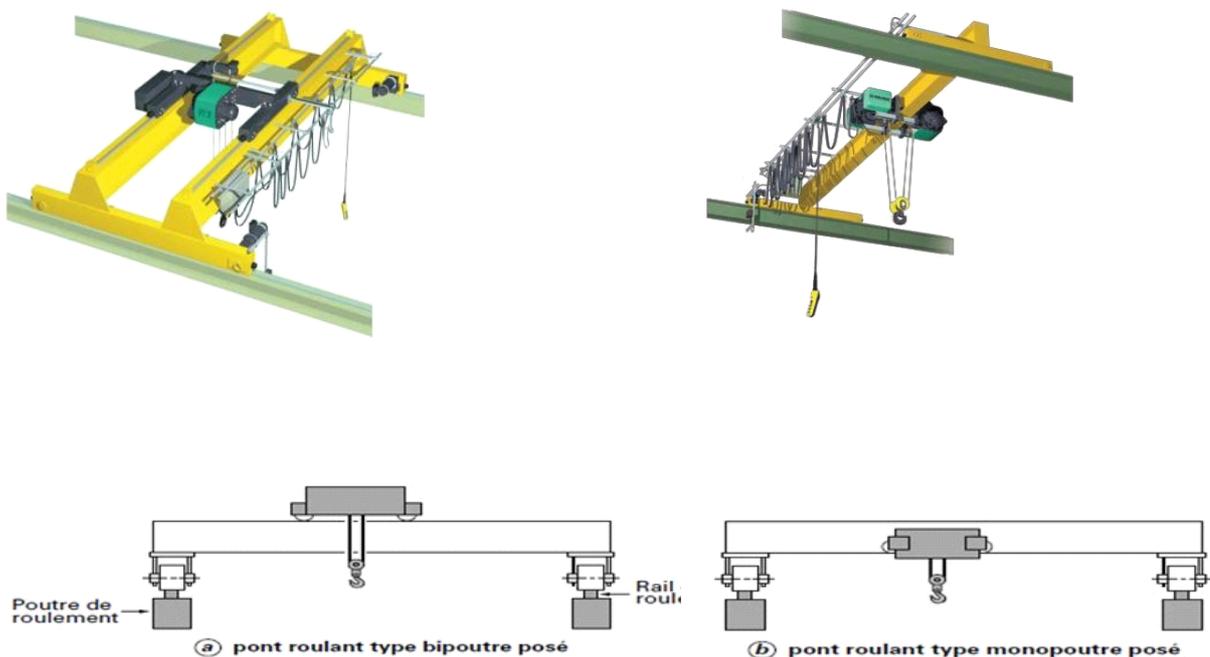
pont roulant (bipoutre et mono-poutre) posé
